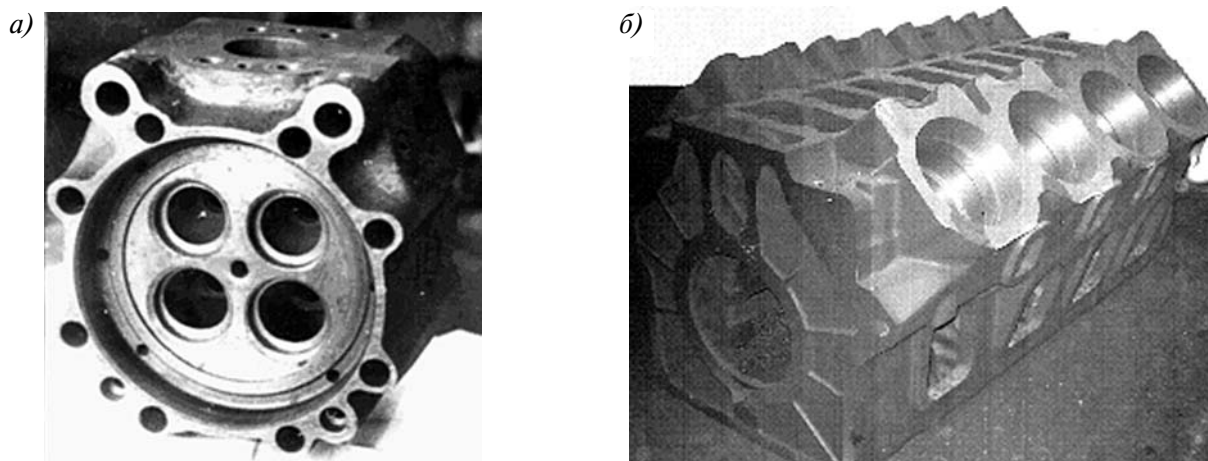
Головка (а) и блок цилиндров (б) из ЧВГ35
